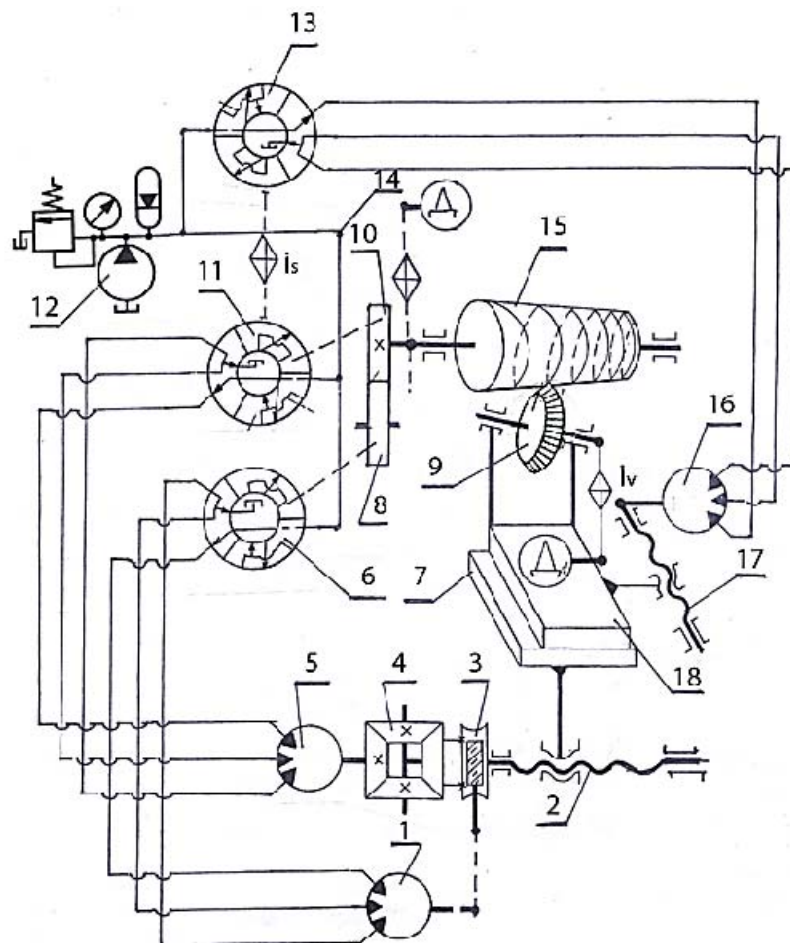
Структурная схема резьбофрезерного станка с гидравлическими формообразующими связями для нарезания конических винтовых поверхностей переменного шага
